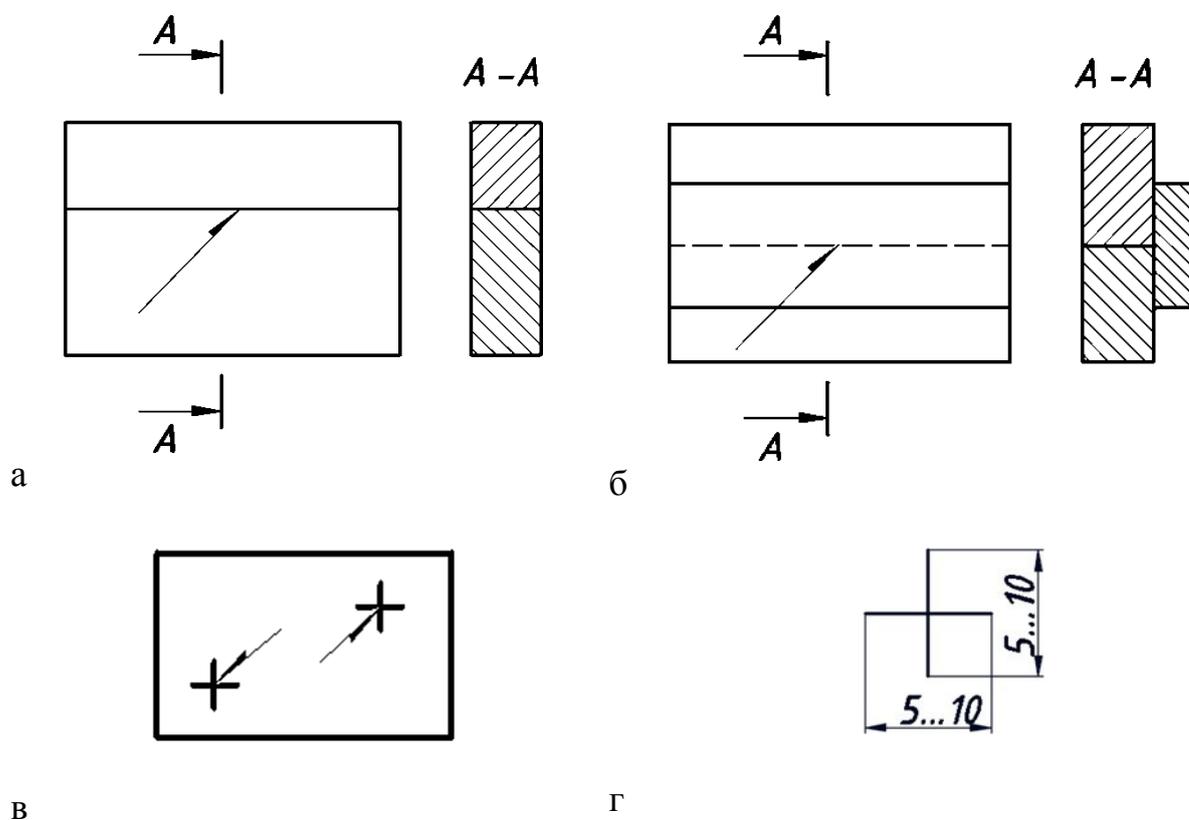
Образец изображения швов сварных соединений.
